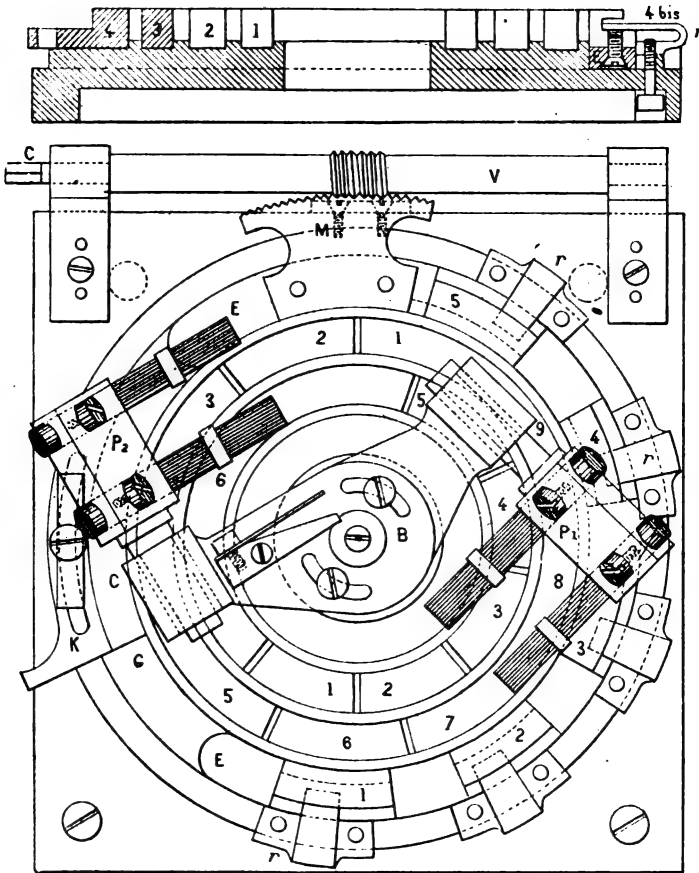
Distributeur Baudot simple. Plan et coupe transversale.
